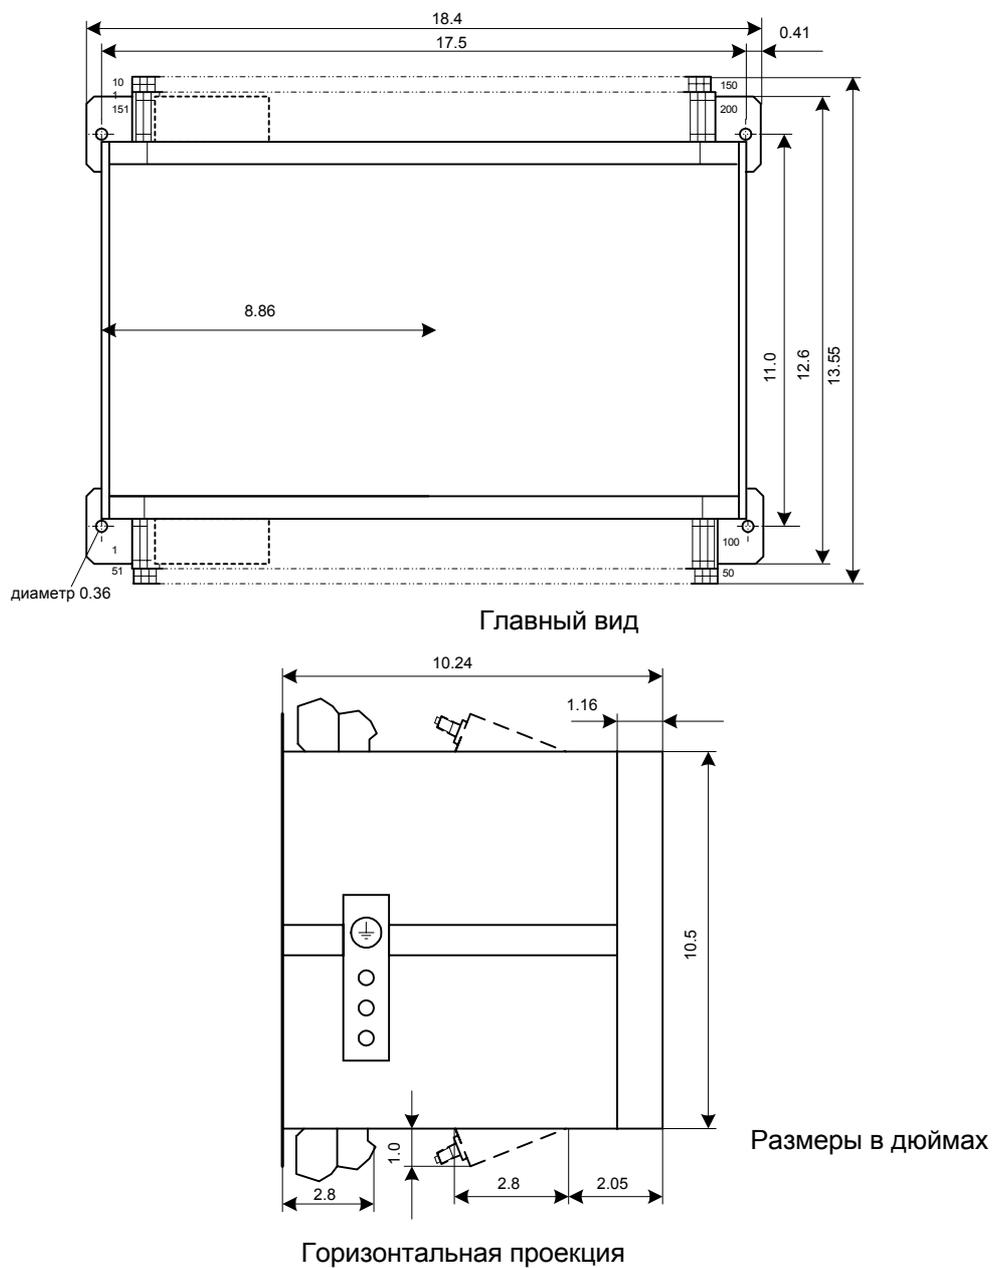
Размеры устройства 7SJ63 для навесной установки на панели
